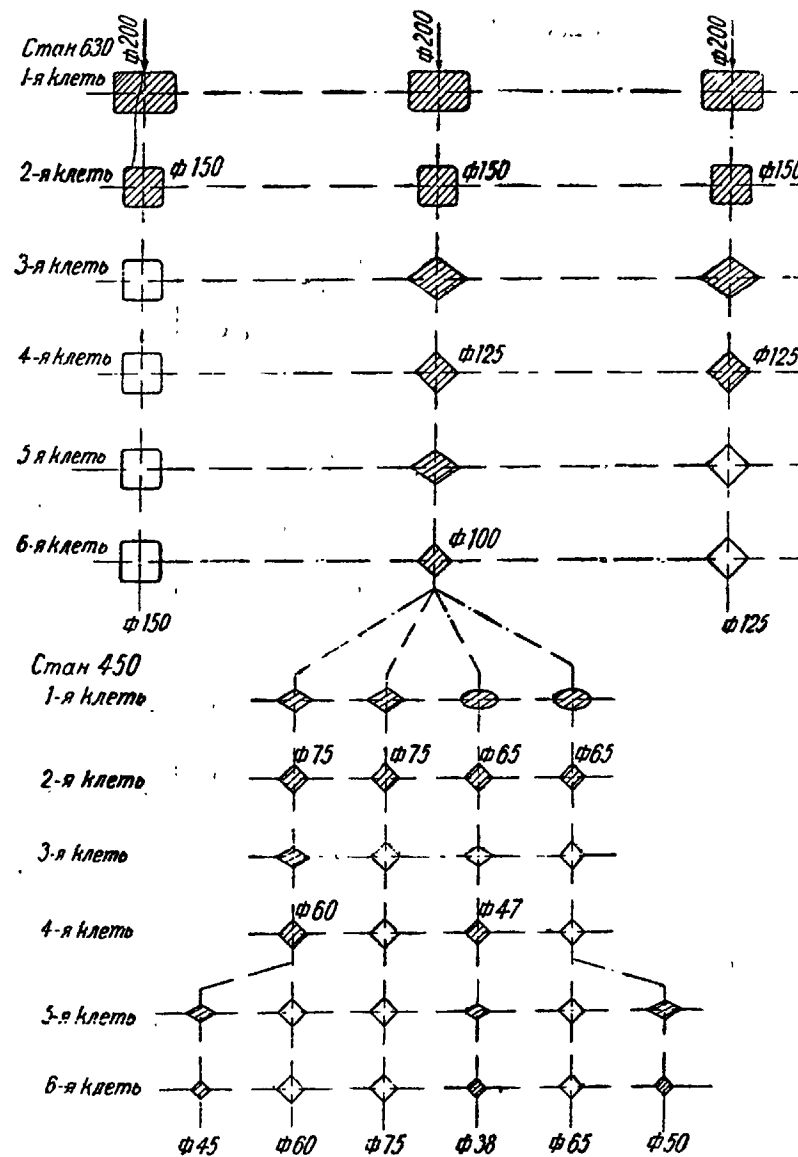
Схема калибровки валков непрерывного заготовочного стана 630—450
